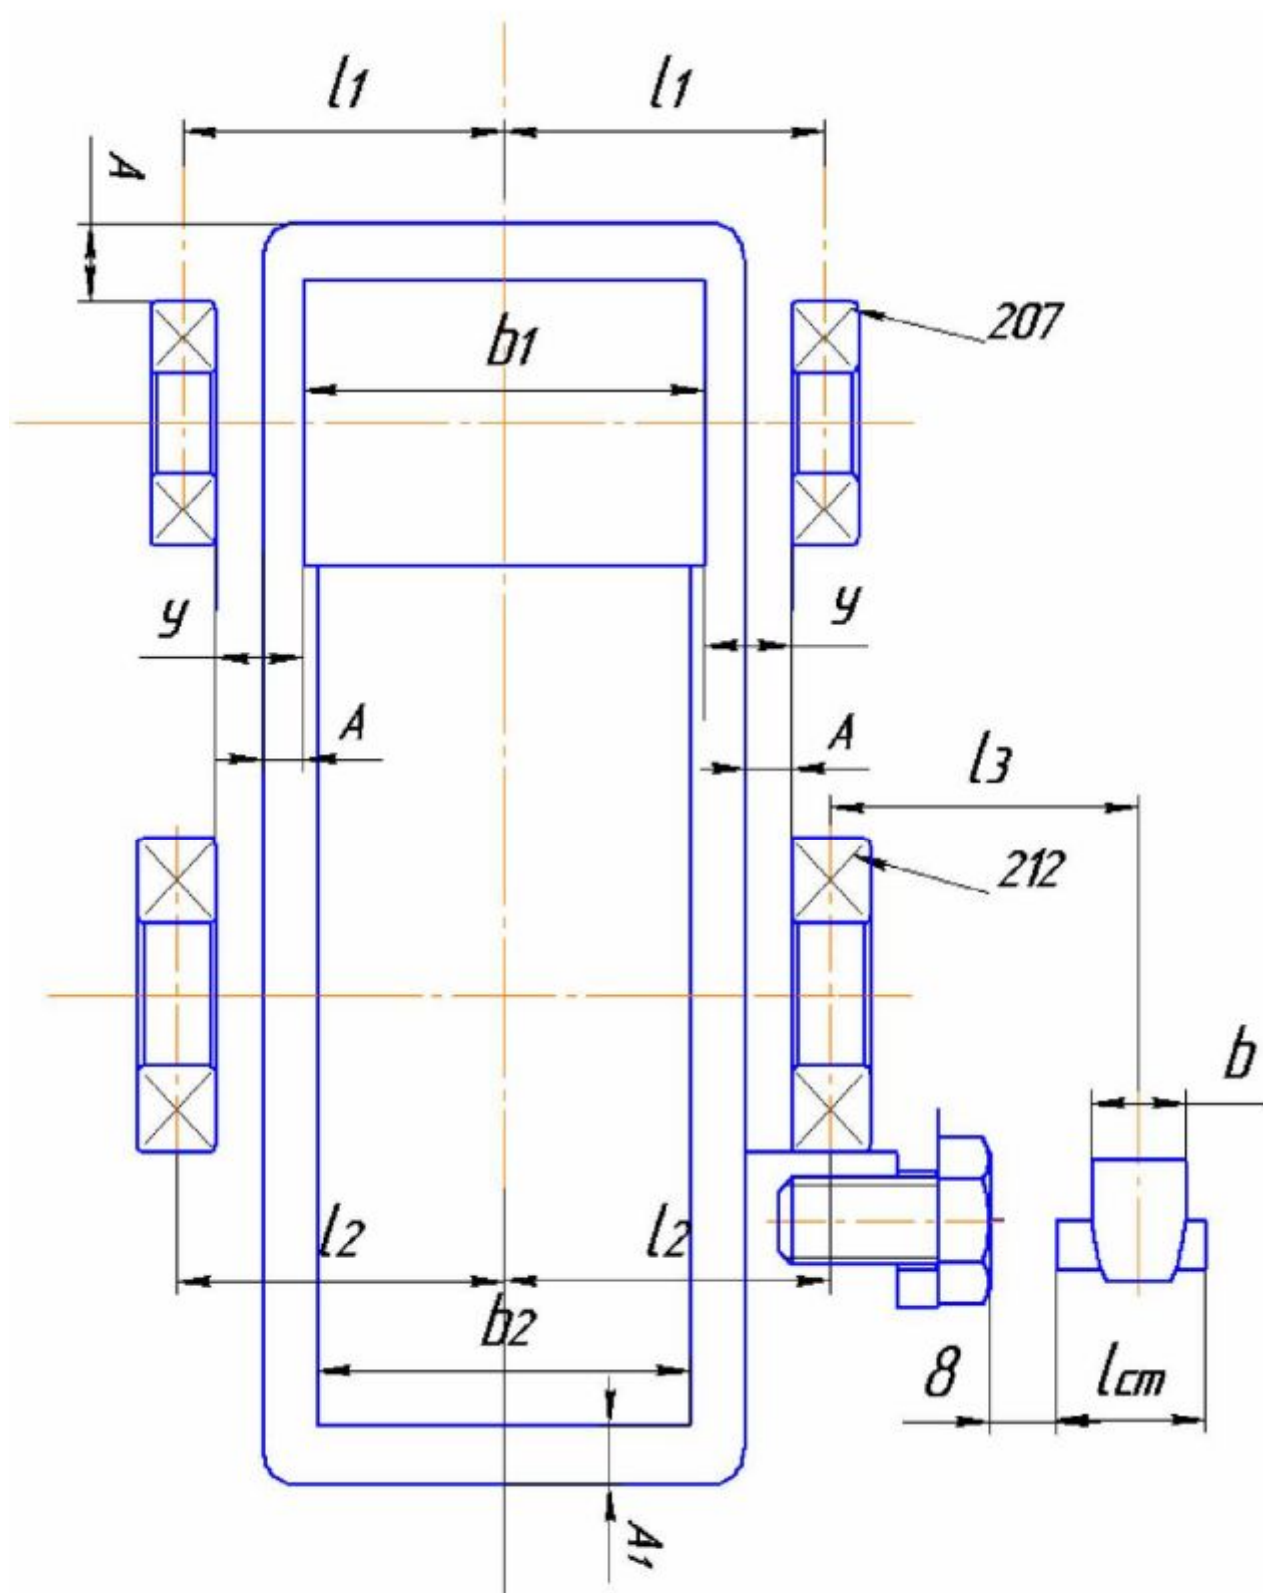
Пример эскизной компоновки цилиндрического редуктора
